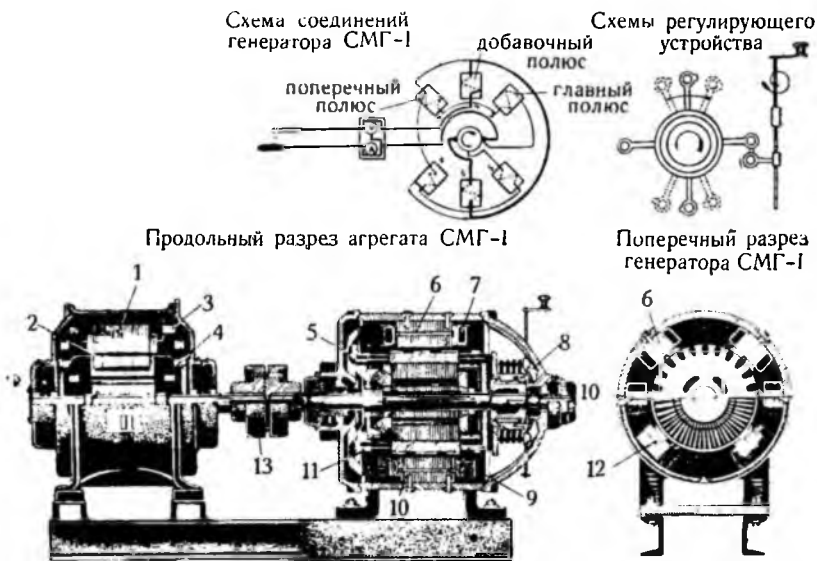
Сварочный мотор-генератор СМГ-1:
